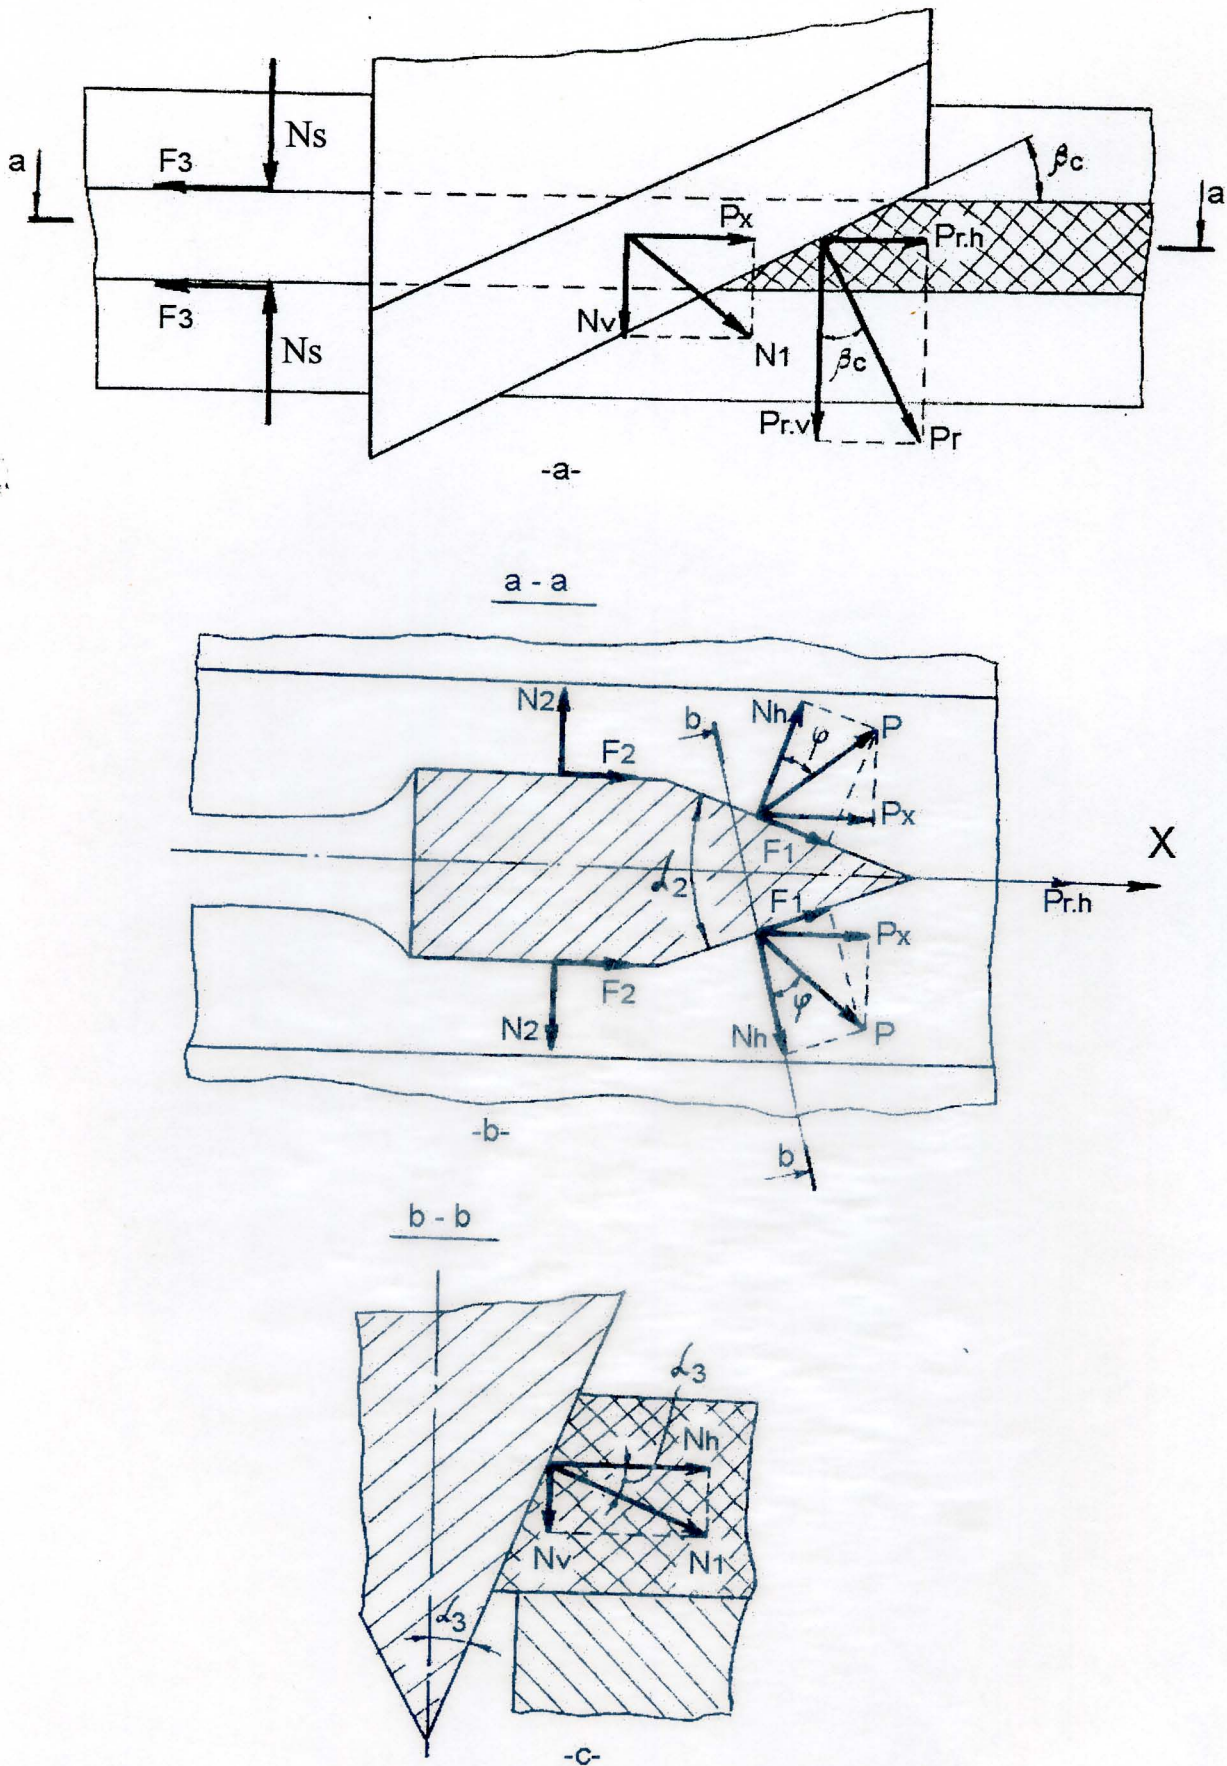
Schéma d'application des forces sur la matière avec un couteau plat incliné.
